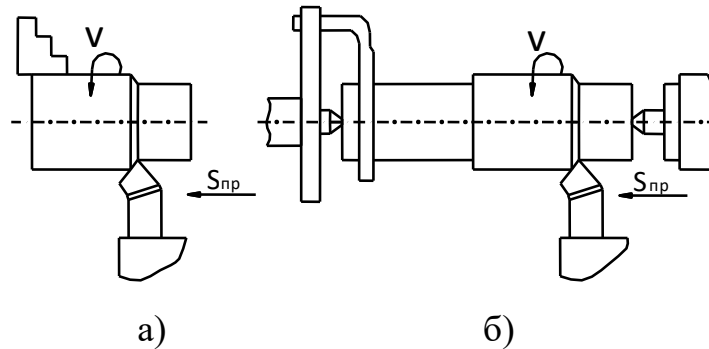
Схеми обточування циліндричних поверхонь
